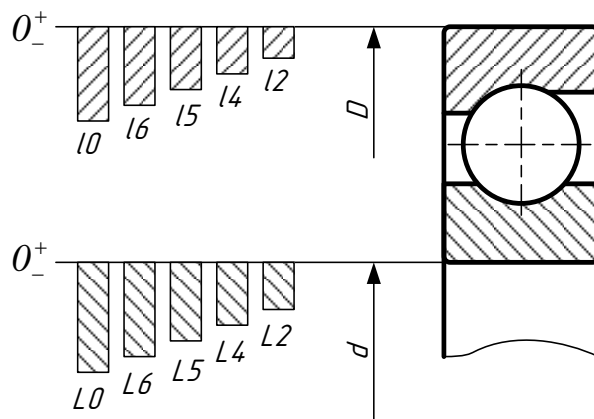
Схема расположения полей допусков на наружный диаметр и диаметр отверстия подшипников по классам точности
